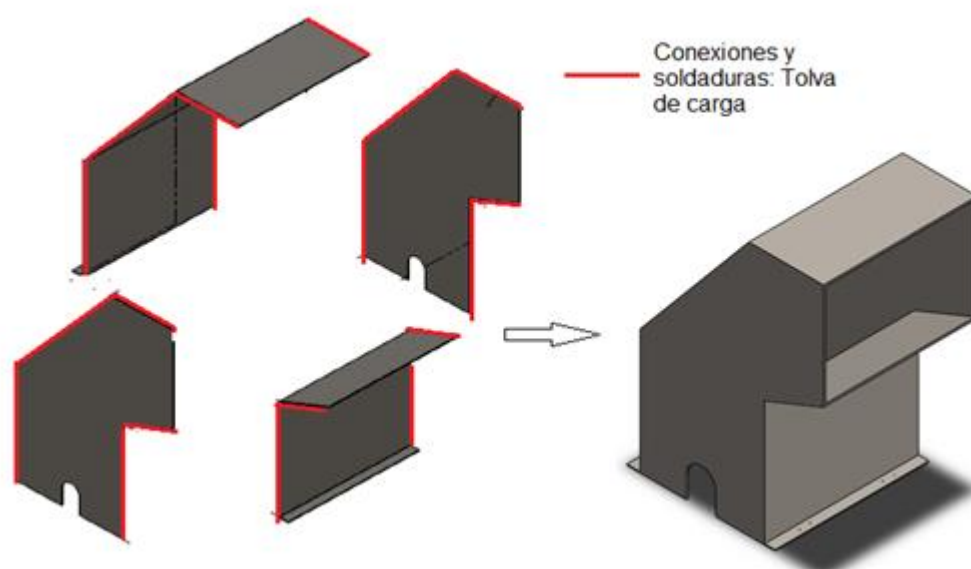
Conexiones y soldadura tolva de carga.
